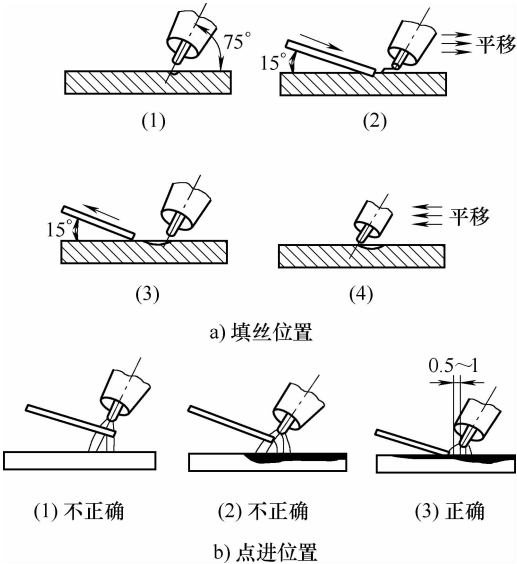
手工钨极氩弧焊的填丝动作和填充焊丝点进的位置
